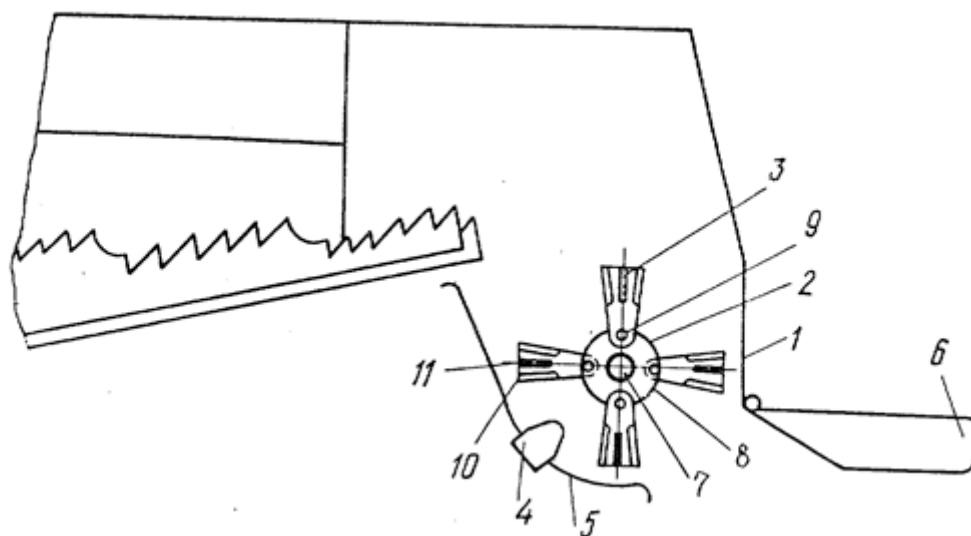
Измельчающий аппарат зерноуборочного комбайна: 1 — корпус; 2 — барабан; 3 — рабочие органы; 4 — противорезы; 5 — лопатка; 6 — разбрасыватель; 7 — вал; 8 — диски; 9 — шарнир; 10 — режущие ножи; 11 — дополнительные кромки лопатки
